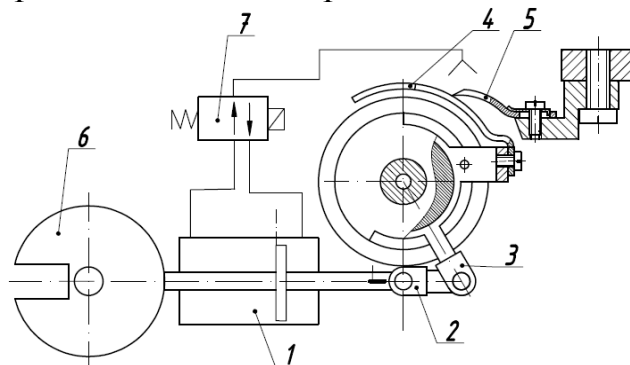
Конструкція механізму обрізки ниток з мехатронним керуванням
